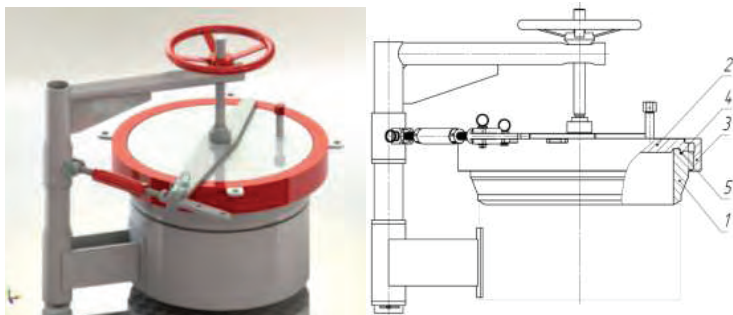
Конструкция резьбового затвора: 1 - фланец резьбовой; 2 - крышка; 3 - гайка накидная; 4 - уплотнительный элемент; 5 - паз.
